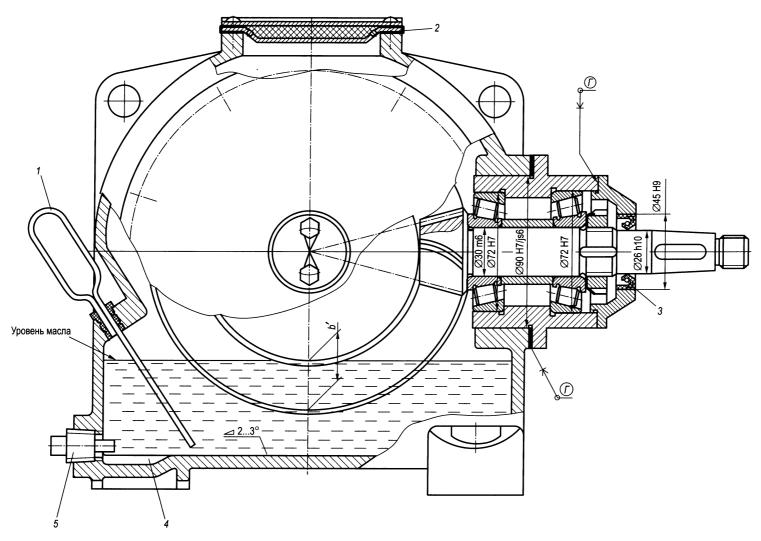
Конический редуктор с погружением колеса в масляную ванну на всю ширину *b*′ зубчатого венца:
